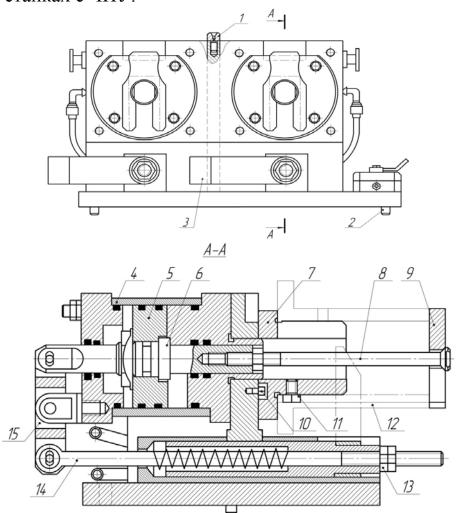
Двухместное специализированное приспособление для установки заготовок деталей типа фланец: 1 — установ; 2 — палец; 3 — прихват; 4 — гидроцилиндр; 5 — поршень; 6 — шток; 7 — сменная наладка; 8 — болт; 9 — быстросменная шайба; 10 — штырь; 11 — винт; 12 — заготовка; 13 — гайка; 14 — тяга; 15 — рычаг
